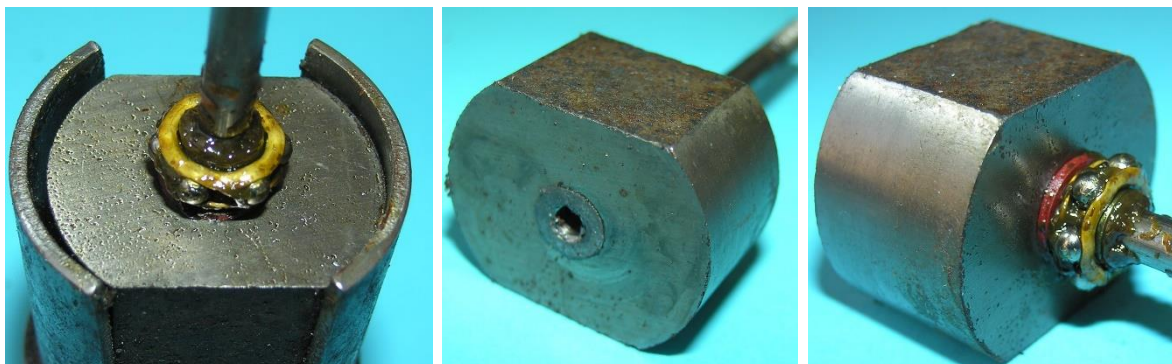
AlNi-Polrad mit den Abmessungen: Durchmesser: 30 mm, Breite: 24 mm, axiale Länge 17 mm
